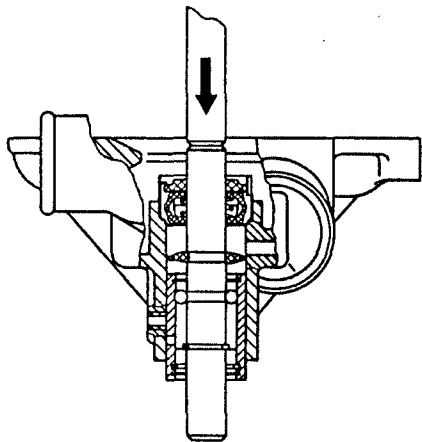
Выпрессовка подшипника с валиком водяного насоса
